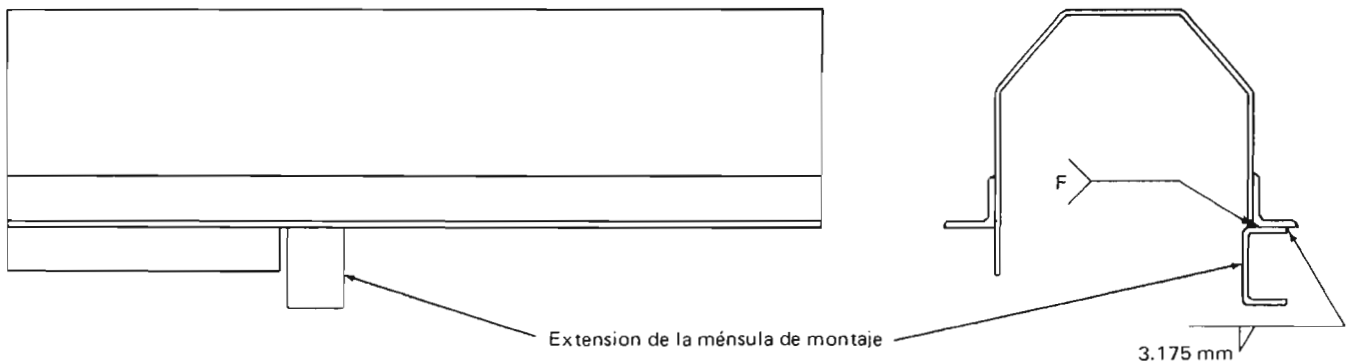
Soldadura suplementaria en las ménsulas de montaje de la jaula protectora del generador auxiliar.
